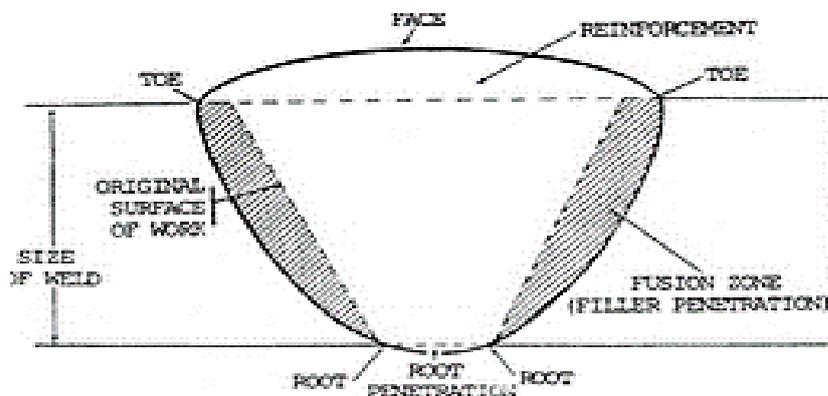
Esquema Soldadura de ranura, junta con bisel en V.
